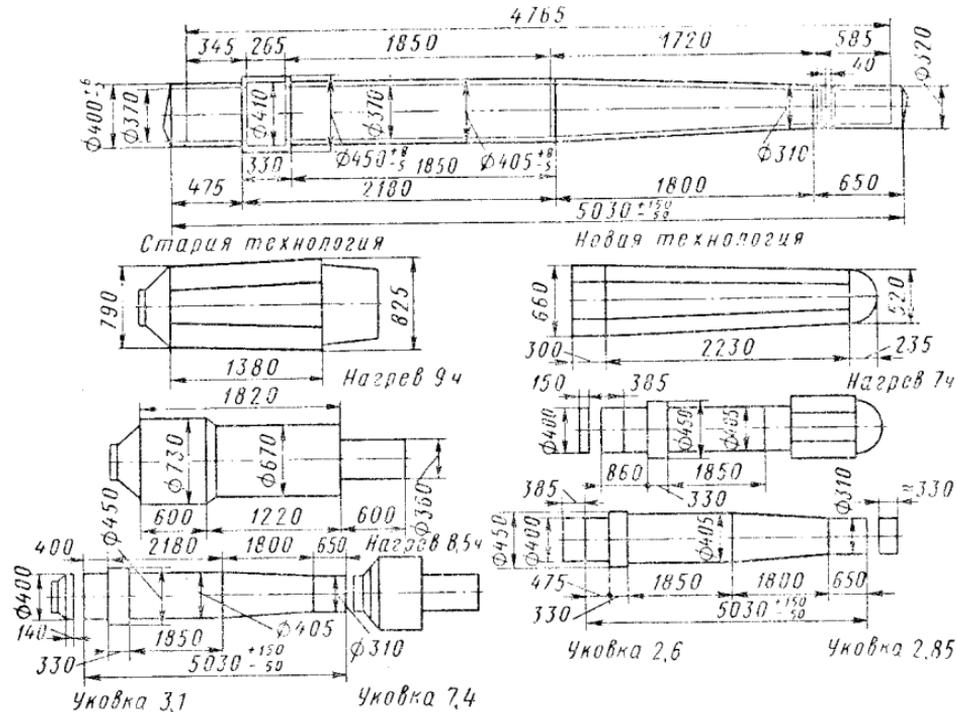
Ковка валов из обычного слитка массой 7320 кг и удлиненного слитка массой 5800 кг
